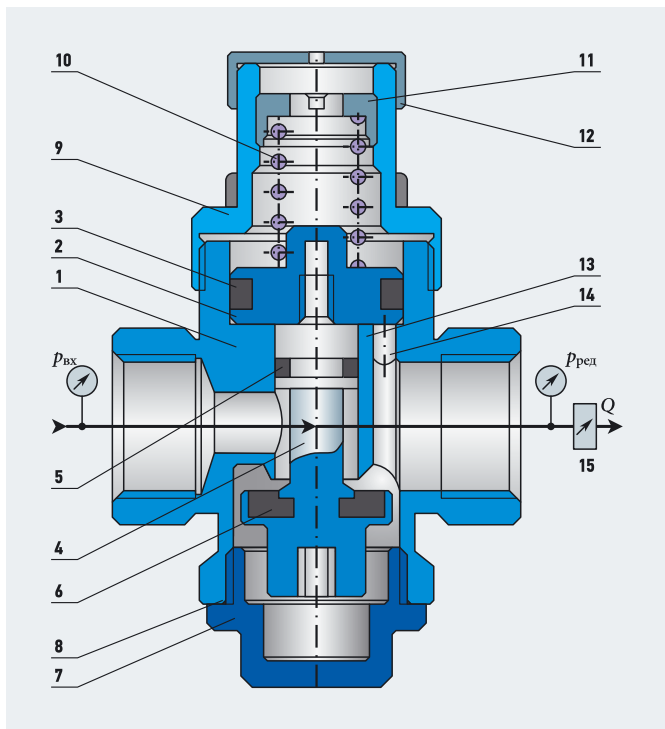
Принципиально-конструктивная схема стандартного поршневого редукционного гидроклапана (1 — корпус; 2 — поршень; 3, 5 — резиновые уплотнительные кольца круглого сечения; 4 — шток с размещенным в его кольцевой канавке резиновым кольцом 5; 6 — завальцованная уплотнительная прокладка; 7 — заглушка; 8 — уплотнительное кольцо круглого сечения; 9 — стакан; 10 — цилиндрическая пружина; 11 — регулировочный винт; 12 — крышка; 13 — седло клапана; 14 — канал, соединяющий подпоршневую полость и полость с редуцируемым давлением  $p_{ред}$ ; 15 — кран в гидравлической линии, по которой вода от редукционного клапана поступает к изливам, сливным устройствам, сеткам и раскателям водоразборной арматуры)
